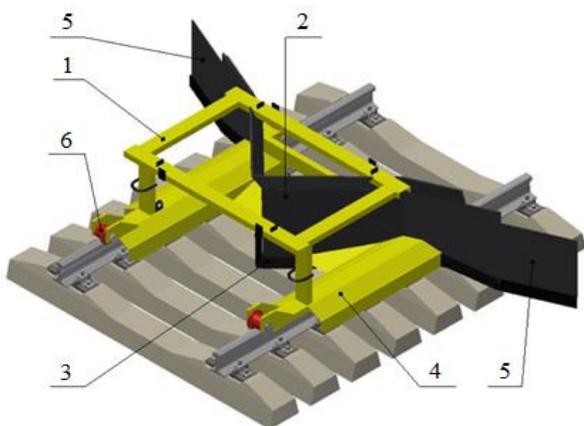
Конструкция устройства для перераспределения и планировки щебеночного балласта:
